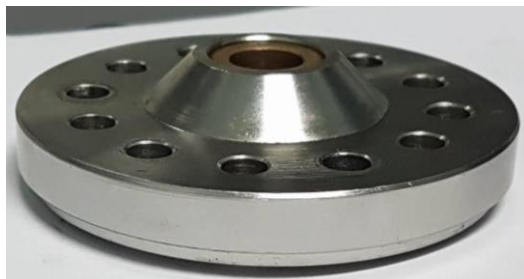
Porta cabezal con cojinete ensamblado. Fuente: Autores.
